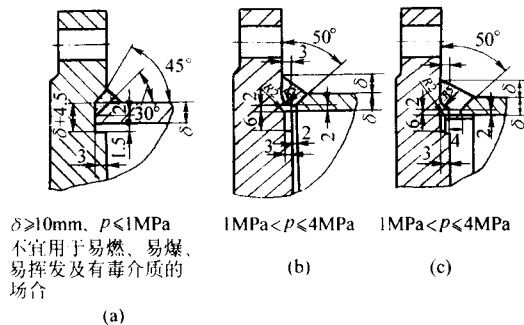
带法兰的管板与筒体连接的焊接接头形式
